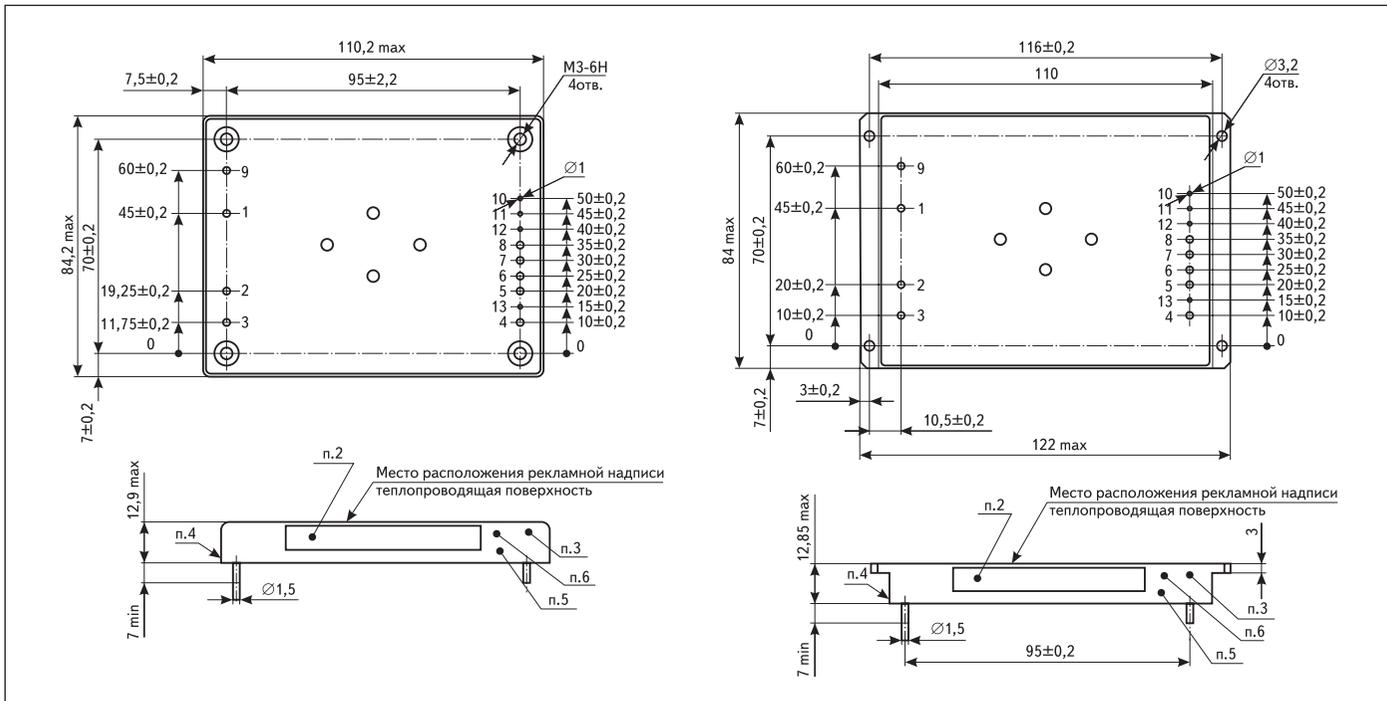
Габаритные чертежи модуля МДМ160-ВТ
